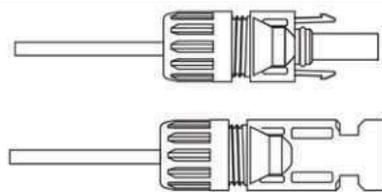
з'єднувач з нагвинченою колпачковою гайкою
